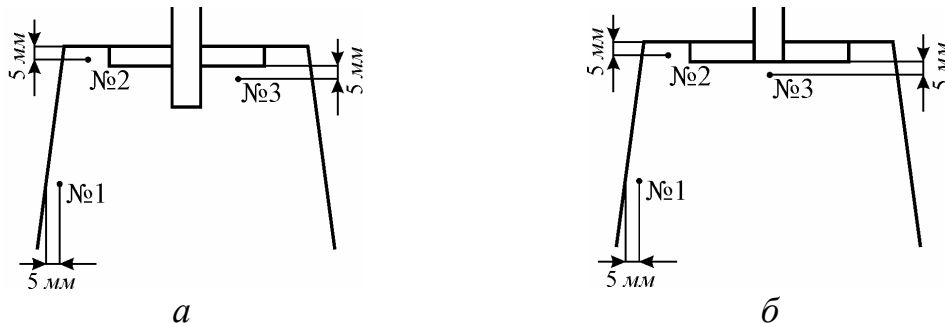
Схема цілнометалевого холодильника (а), корпусного холодильника з утеплювальною вставкою (б) та розташування термопар №№ 1 – 3
